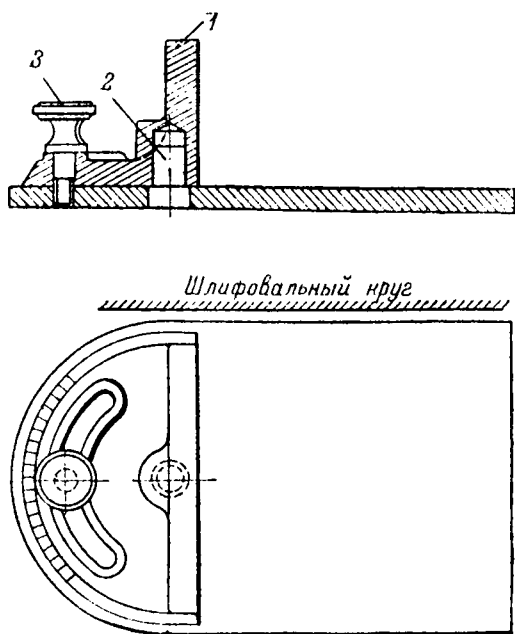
Приспособление для установки изделий, шлифуемых под прямым углом
